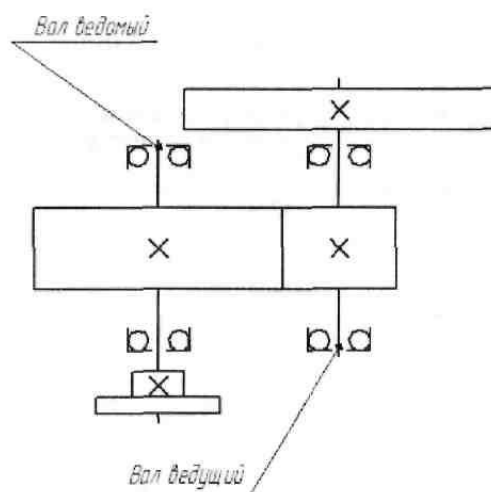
Кинематическая схема редуктора одноступенчатого цилиндрического-АБВГ.303115.094
